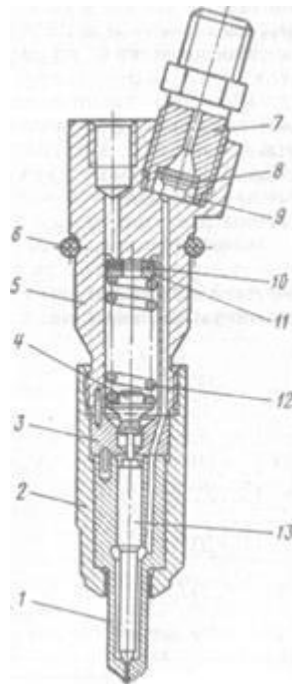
Форсунка двигунів КАМАЗ: 1 – розпилювач; 2 – гайка; 3 – проставка; 4 – штанга; 5 – корпус; 6 – кільце ущільнювача; 7 – штуцер; 8- фільтр; 9 – втулка; 10 – регулювальні шайби; 11 – опорна шайба; 12 - пружина; 13 – голка розпилювача.
